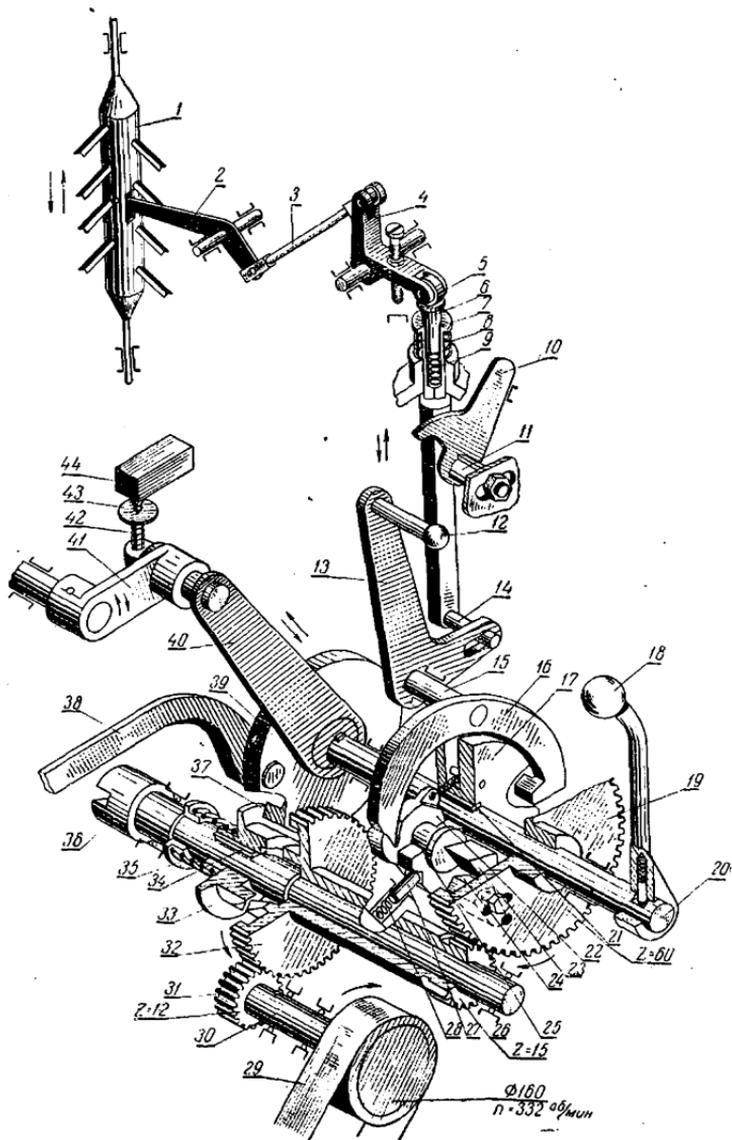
Кинематическая схема механического автомата вальцового стапка ЗМ.
